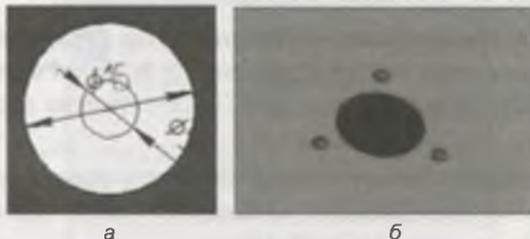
Эскиз подшипника (а); созданный подшипник (б)
